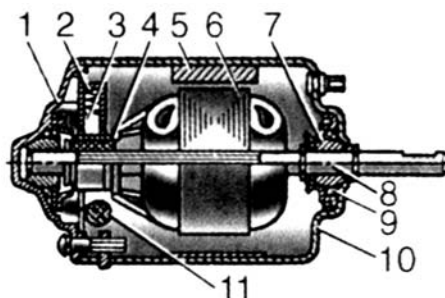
Электродвигатель 197.3730: 1 – крышка; 2 – пружина; 3 – щетка; 4 – коллектор; 5 – магнит; 6 – якорь; 7 – подшипник; 8 – вал; 9 – фетровая шайба; 10 – корпус; 11 – фильтр радиопомех
